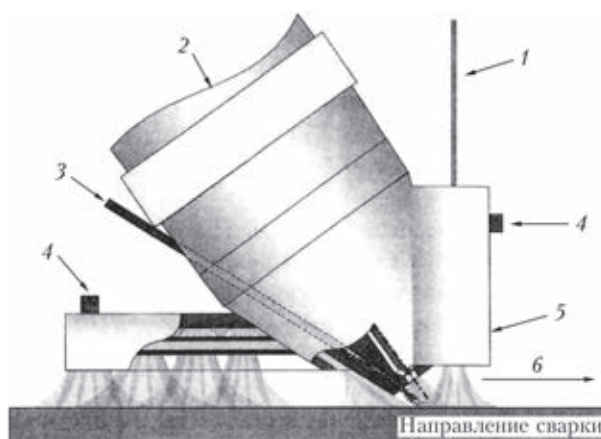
Схема гибридной лазерно-плазменной сварки с плазменной дугой прямого действия и порошковой присадкой [17]: 1 — лазерное излучение; 2 — плазмообразующий газ; 3 — порошок с транспортирующим газом; 4 — защитный газ; 5 — трубка, через которую подается излучение; 6 — направление сварки
